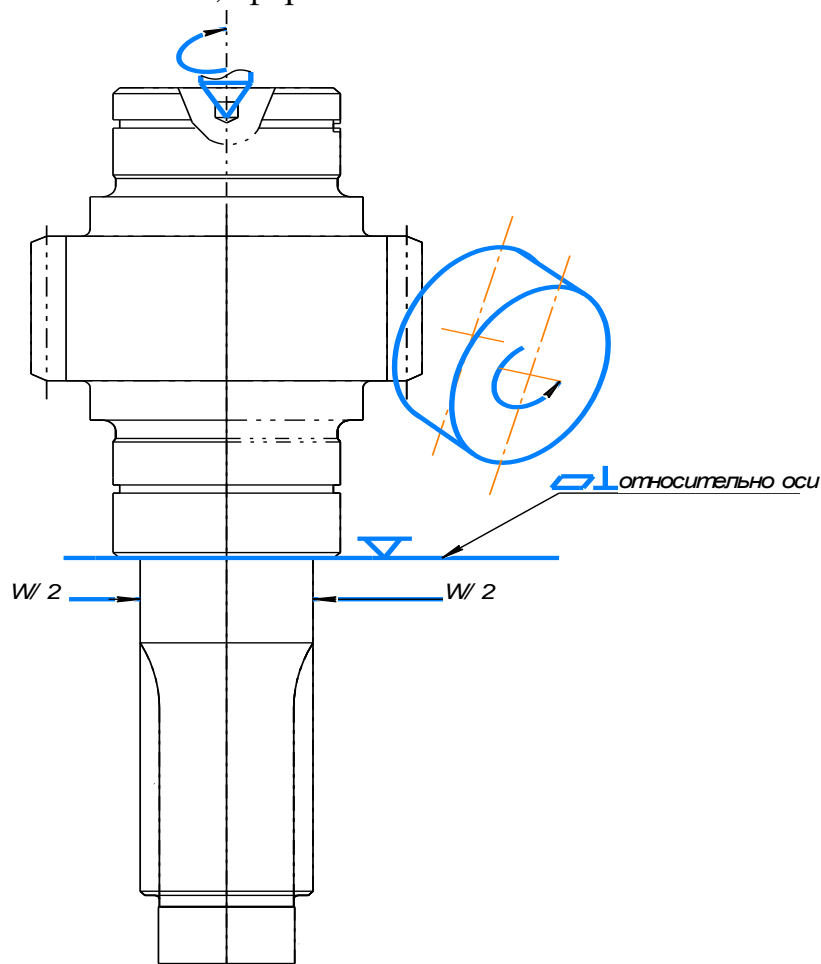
Принципиальная схема приспособления при обработке на зубофрезерном станке с ЧПУ HGH-180
